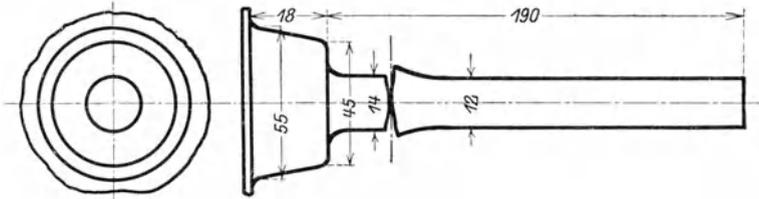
Kegel im Gesenk geschmieden, Rundeisen anschweißen.
